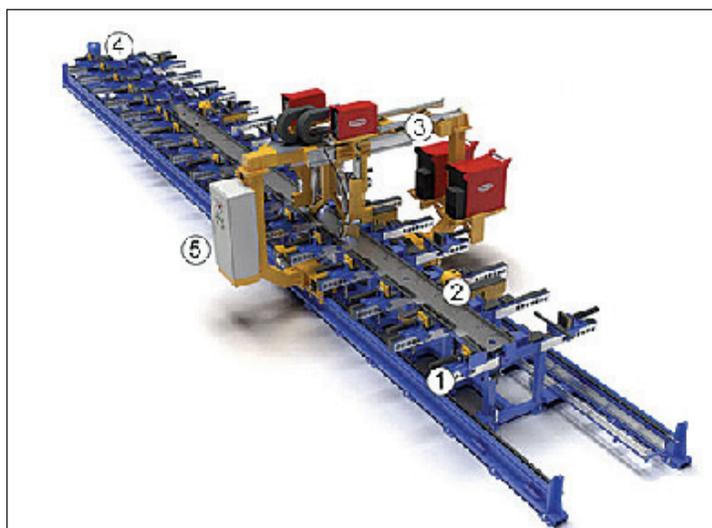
Общий вид линии сборки и сварки лонжеронов: 1 — стенд для сборки лонжеронов; 2 — кантователь; 3 — сварочный портал; 4 — гидростанция; 5 — шкаф управления
